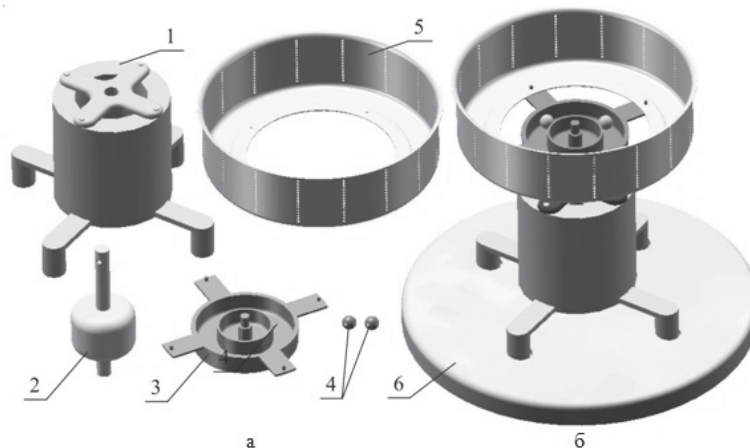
Комп'ютерна 3D модель СВ (а – основні деталі СВ; б – збірка СВ)
